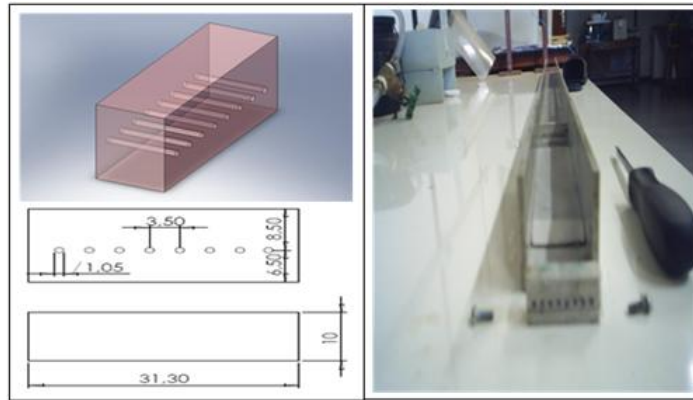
Detalhamento esquemático do bloco-guia de oito fios de *SMA* (dimensões em mm).
